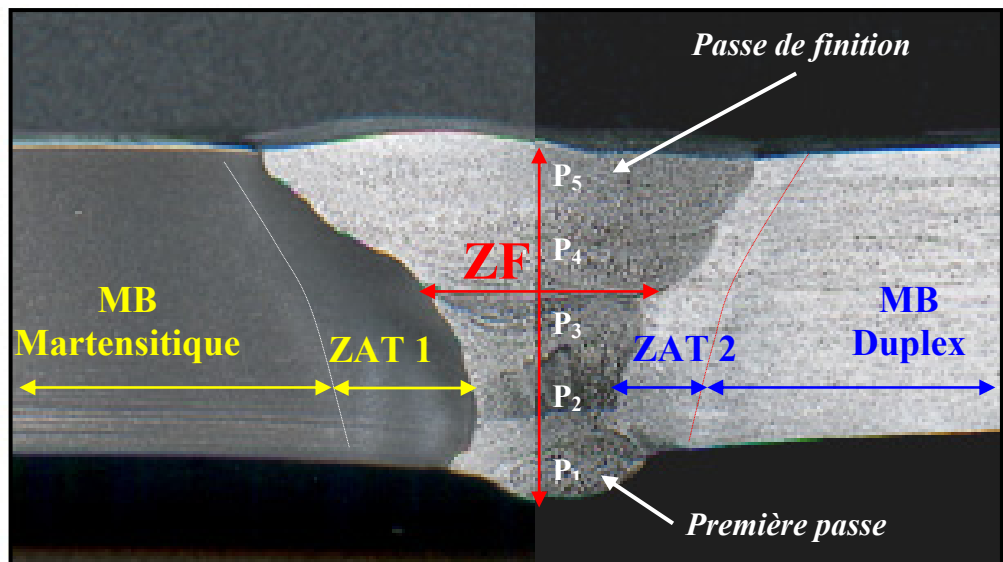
illustration macrographique du joint soudé et ses zones principales.
